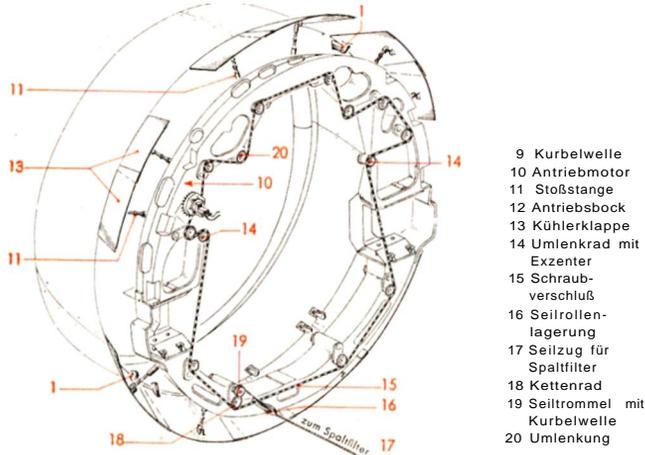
Motorspant I in Gußausführung mit Kühlerklappenbetätigung
